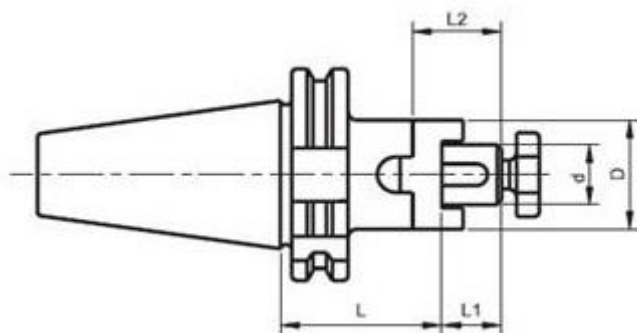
Оправка для торцевой фрезы DIN69871 форма SK
